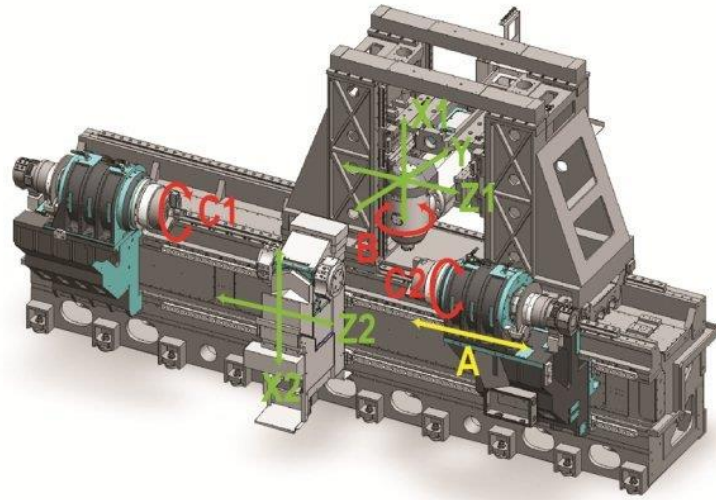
Координаты станка Takisawa TMT 4500 TT
